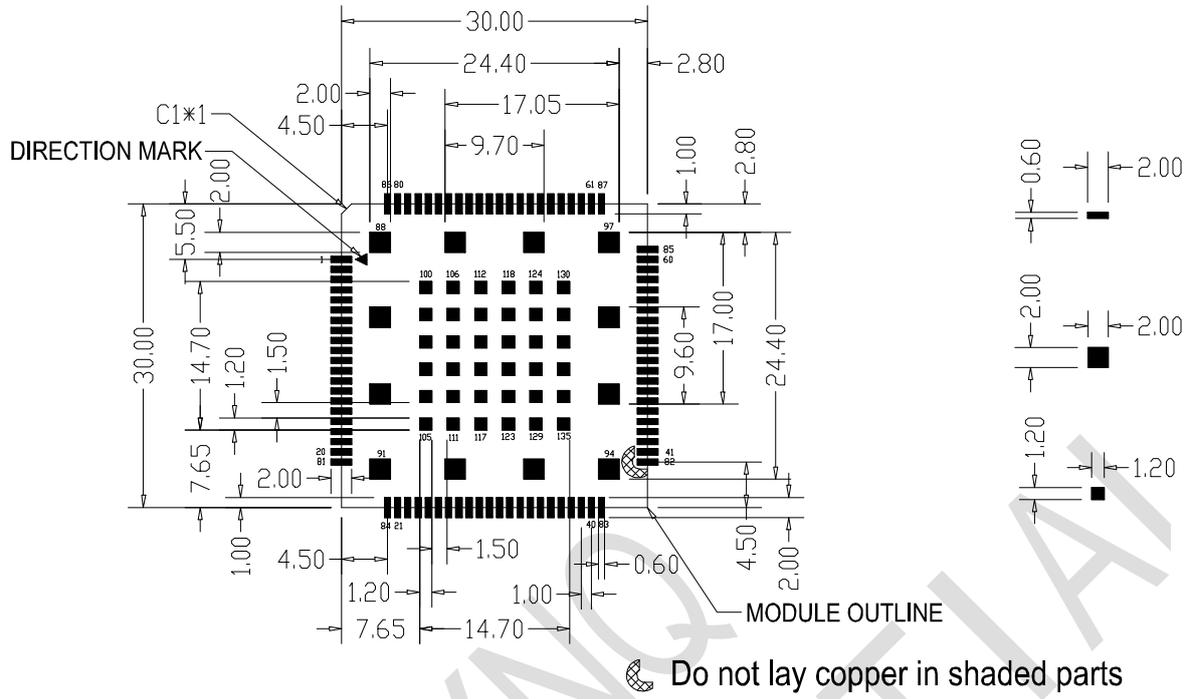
模块推荐焊盘 (Top view 单位: mm)
